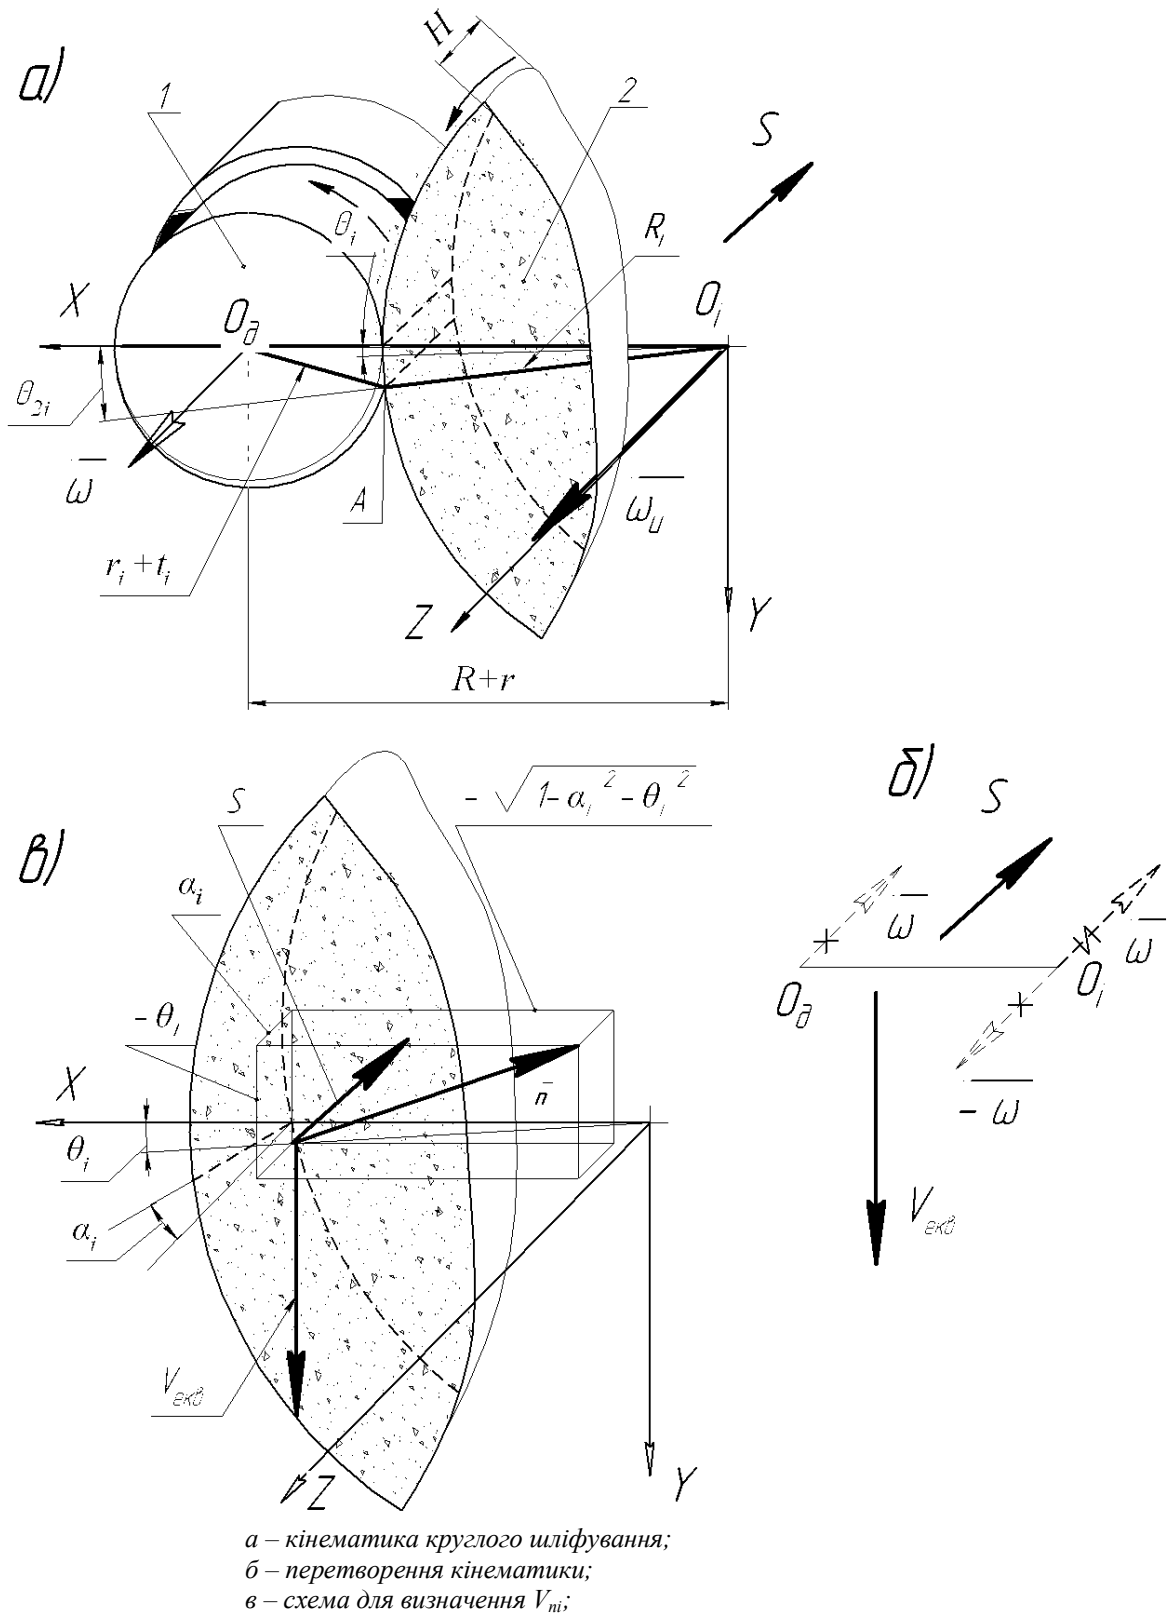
Схема круглого поздовжнього глибокого шліфування
